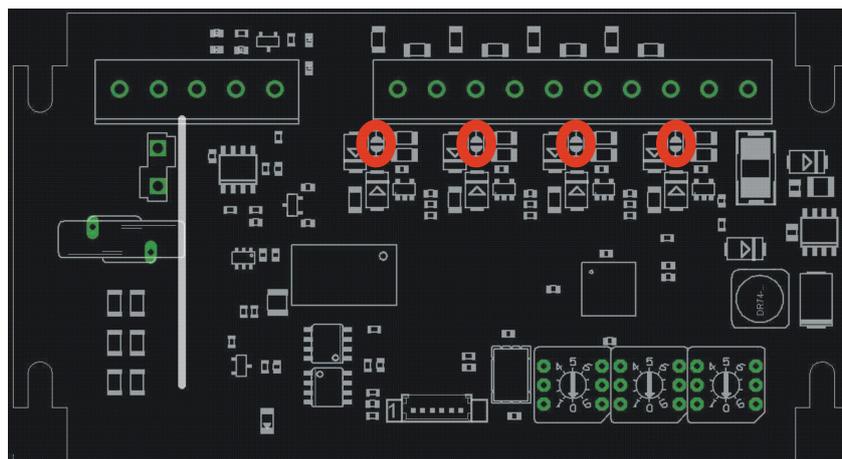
MaxiDimm3000-PCB mit Markierungen für Lötbrücken
